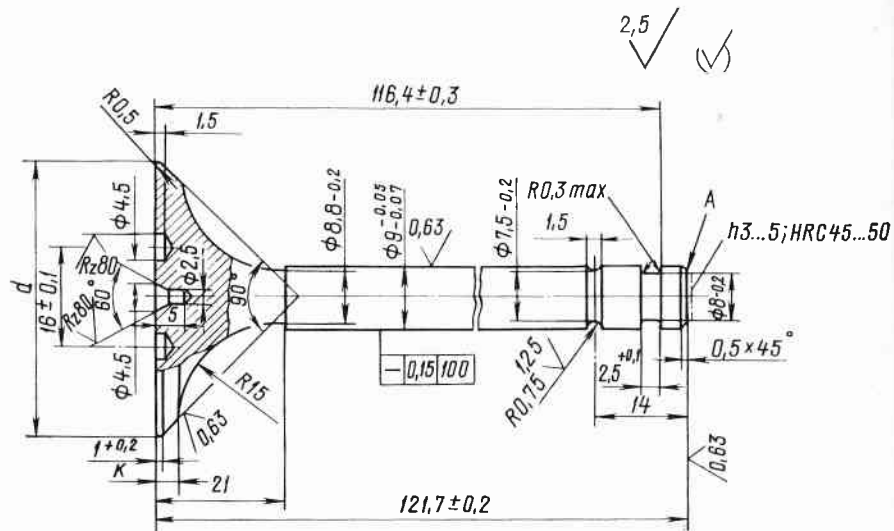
Клапан всасывающий — 10Д6—16.00.14
